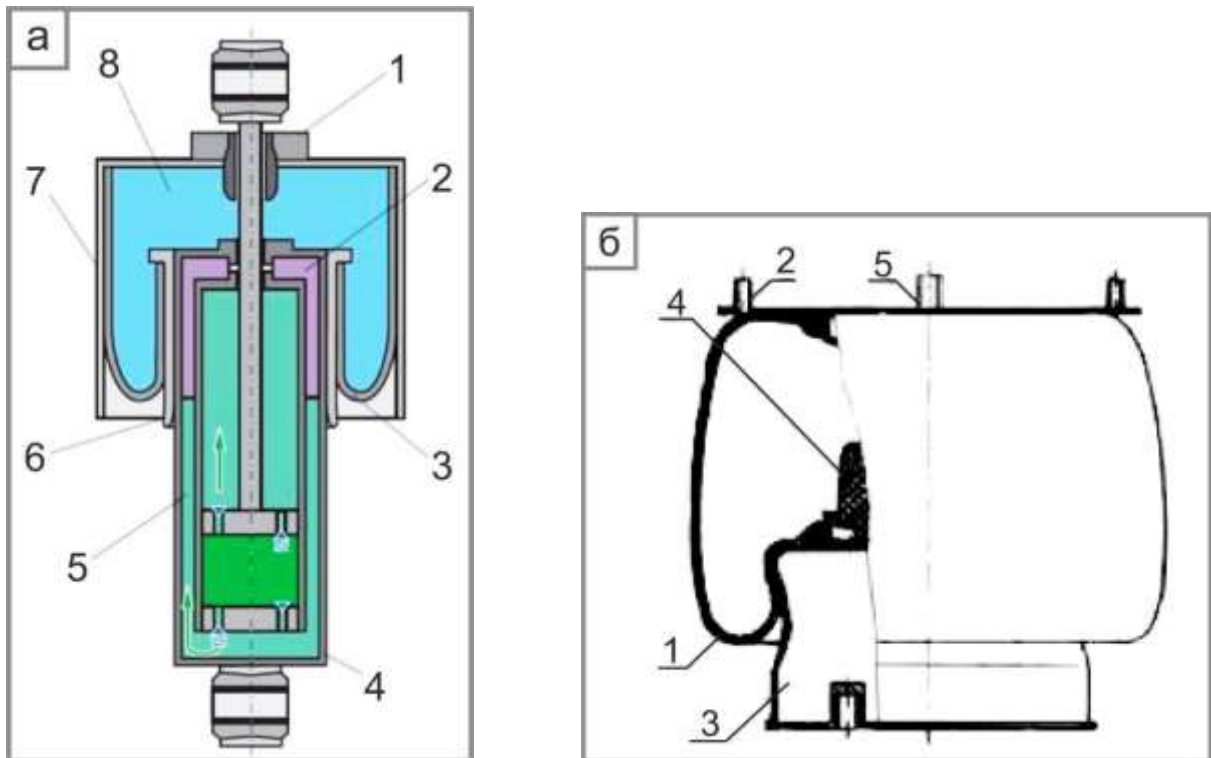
Пневматичні пружні елементи: *а* - з вбудованим амортизатором (пневморесора): 1 – корпус; 2 – газова порожнина амортизатора; 3 – манжета (рукав); 4 – двотрубний газонаповнений амортизатор; 5 – компенсаційна порожнина амортизатора; *б* – поршень; 7 – напрямна корпусу; 8 – повітряна порожнина; *б* – пневмобалон: 1 – гумово-кордна оболонка; 2 – верхній фланець; 3 – поршень; 4 – гумовий буфер; 5 – штуцер для підведення стисненого повітря
